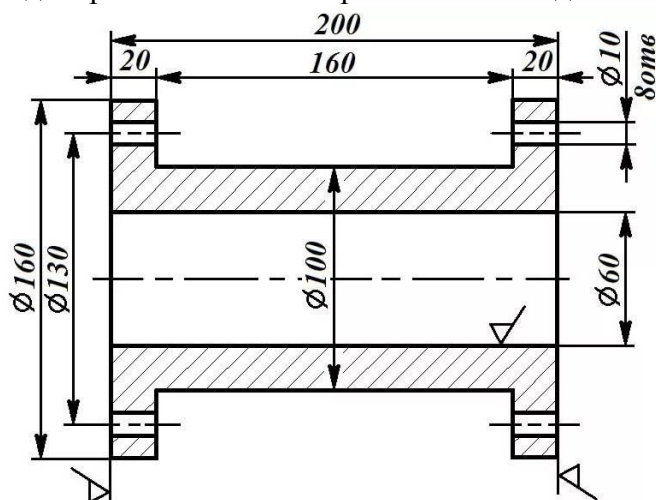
Эскиз детали «Патрубок», материал – сталь 40ХН.
